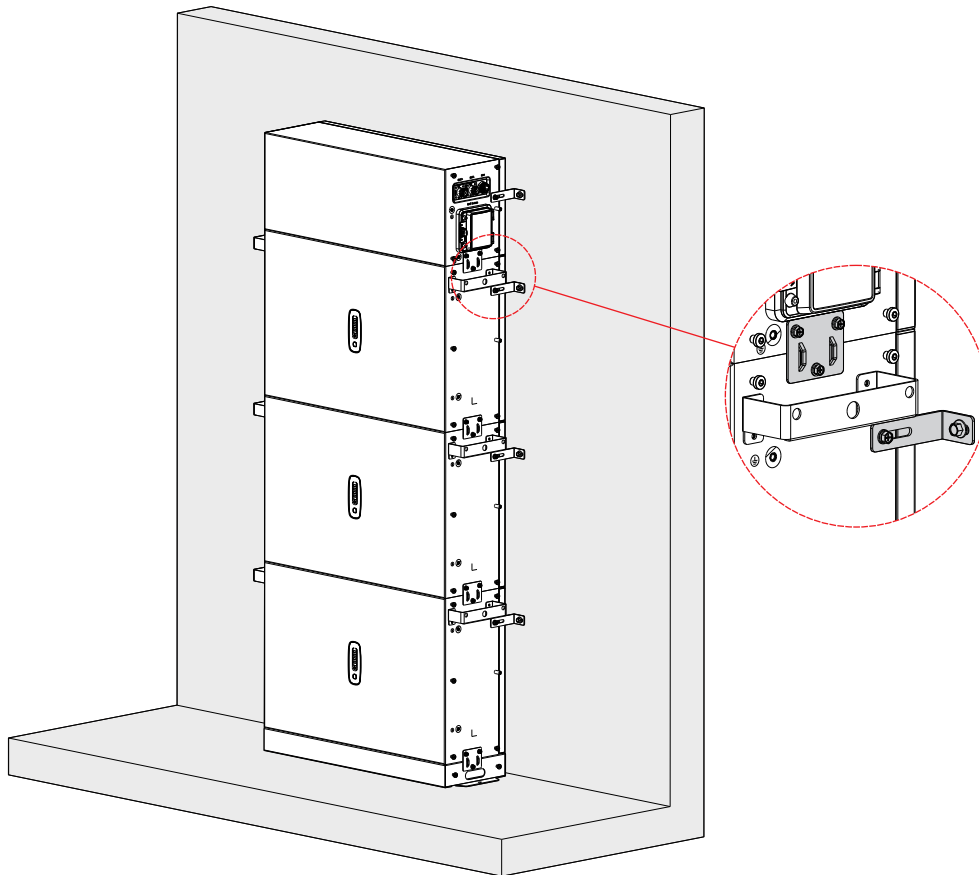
Posizionamento dei moduli batterie per fissare le staffe alla parete
